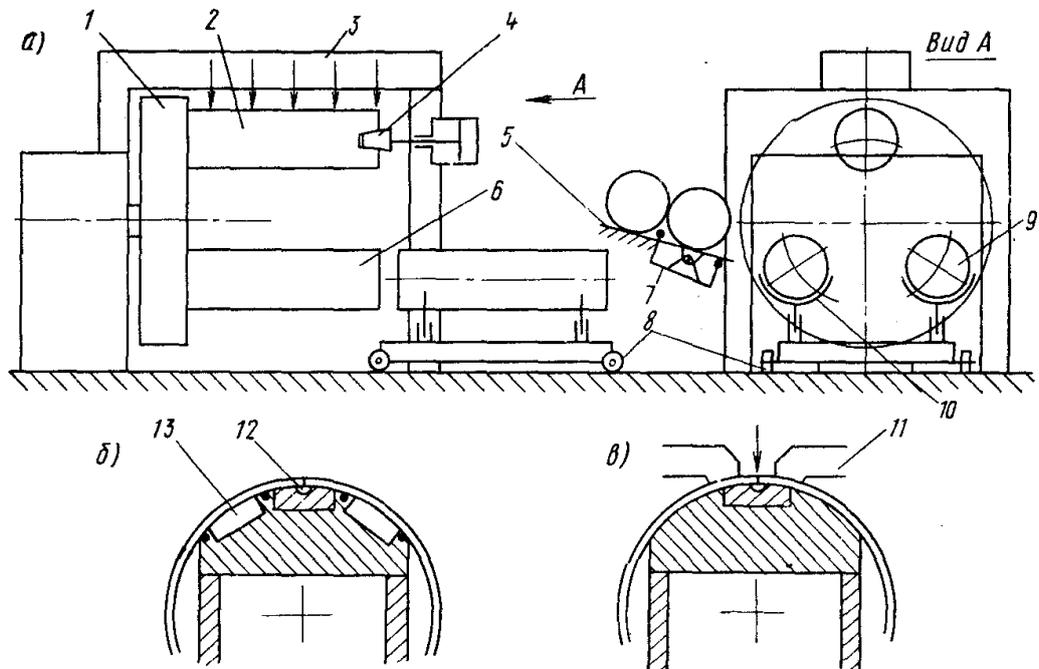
Полуавтоматическая установка для сборки и сварки
